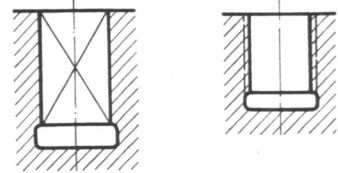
und 239. Aussparungen in Rücksicht auf das Auslaufen der Werkzeuge.
